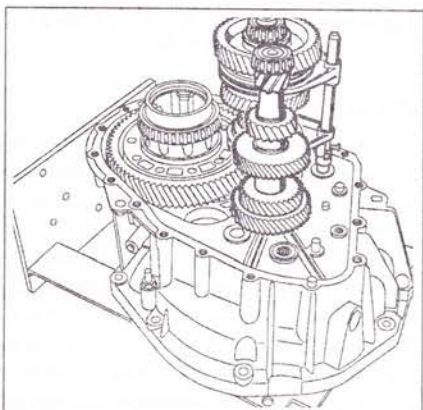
Снимите сборку длинного вторичного вала с вилкой и первичный вал.
